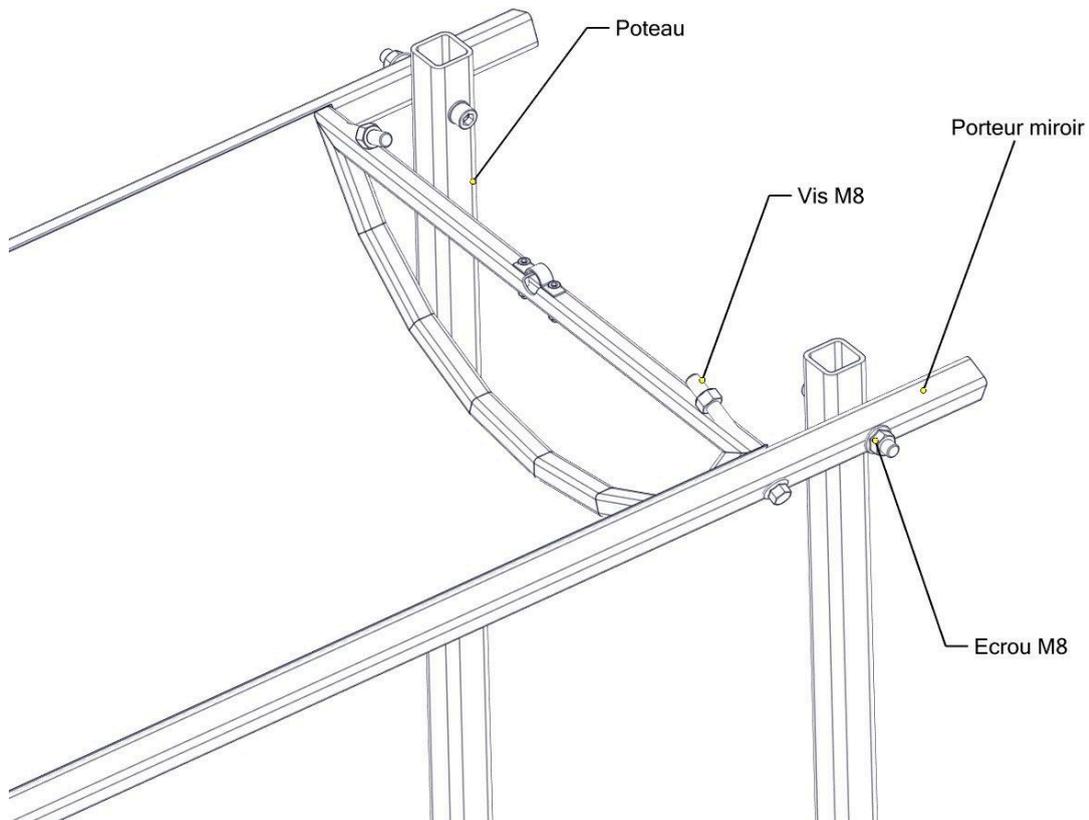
Illustration des poteaux, porteurs miroir et visserie de fixations
